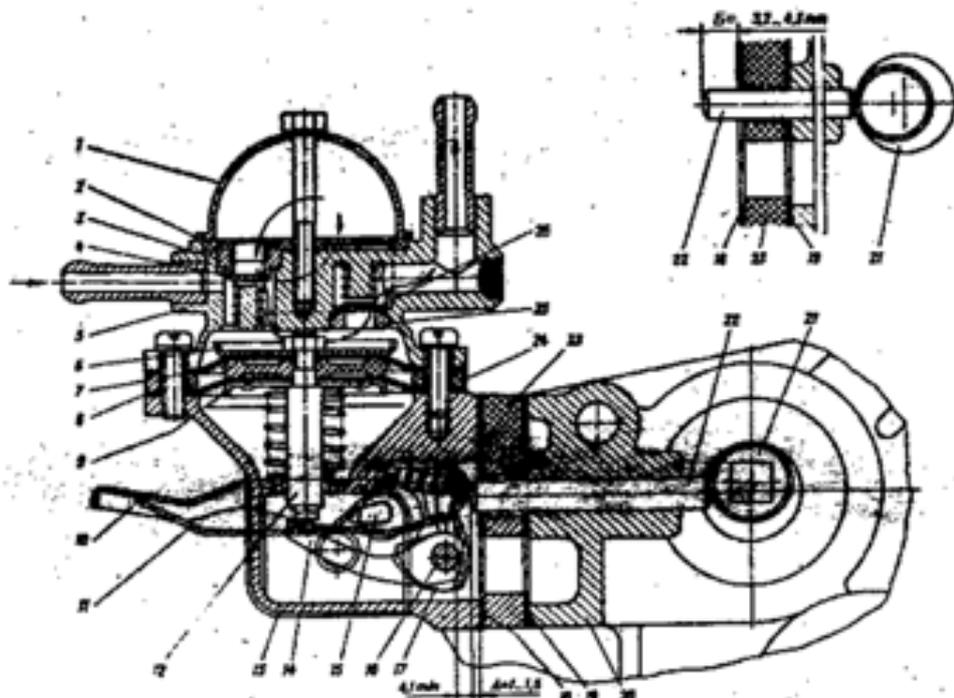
Бензиновый насос: 1 - крышка; 2 - фильтр; 3 - пробка седла впускного клапана; 4 - впускной клапан; 5 - верхний корпус; 6 - чашечка верхняя диафрагмы; 7, 24 внутренняя и наружная дистанционные прокладки; 8 - диафрагма; 9 - чашечка нижняя диафрагмы; 10 - рычаг; 11 - пружина рычага; 12 - шток; 13 - нижний корпус; 14 - балансир; 15 - эксцентрик; 16 - ось рычага и балансира; 17 - рычаг заполнителя; 18 - уплотнительная прокладка; 19 - уплотнительно-регулирующие прокладки; 20 - корпус привода; 21 - кулачок привода; 22 - штанга; 23 - проставка; 25 - пробка седла нагнетательного клапана; 26 - нагнетательный клапан; Б - величина выступа штанги; А - величина утопания рычага до начала рабочего хода
